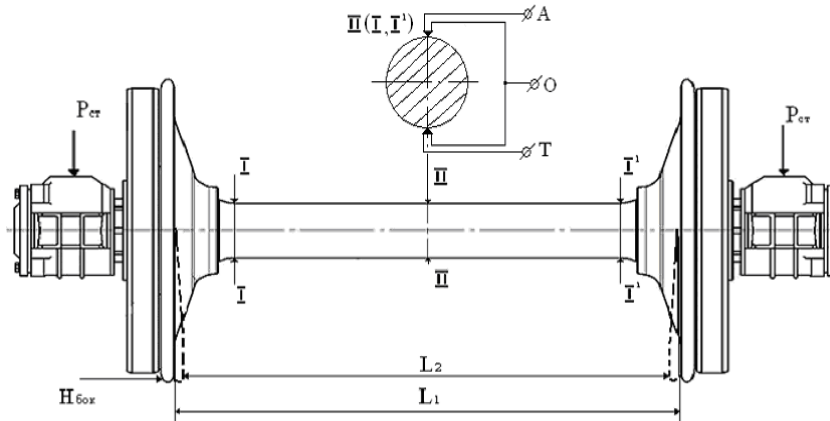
Схема приложения испытательных нагрузок при стендовых испытаниях
